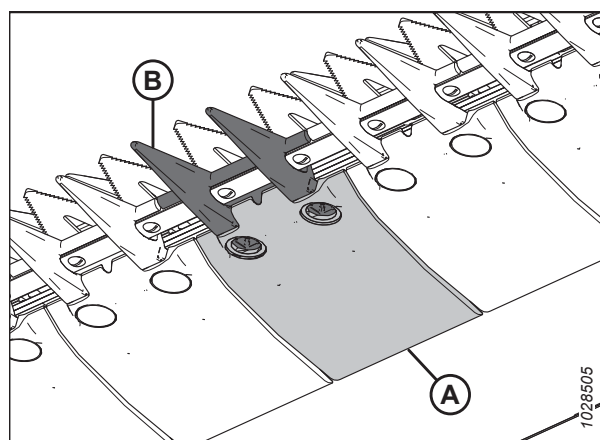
Укороченный противорежущий палец и износная пластина
